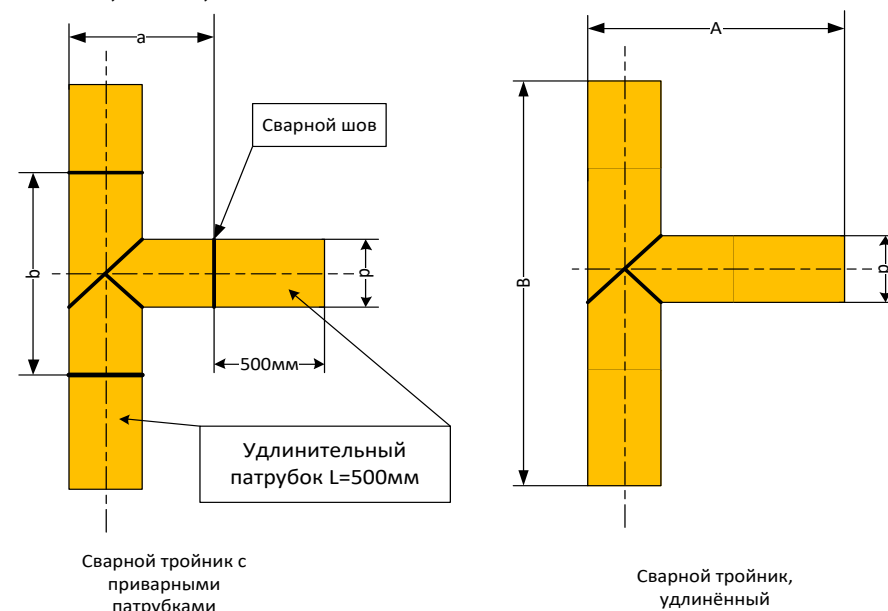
Варианты исполнения соединений полиэтиленовых труб и фитингов (сварной тройник с приварными патрубками)
